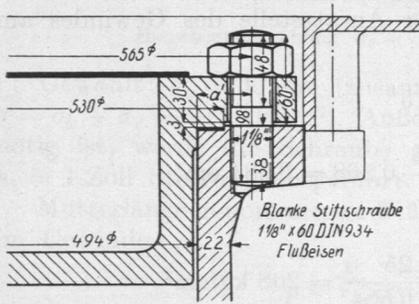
Flanschverbindung mittels Stiftschrauben. M. 1:4.
